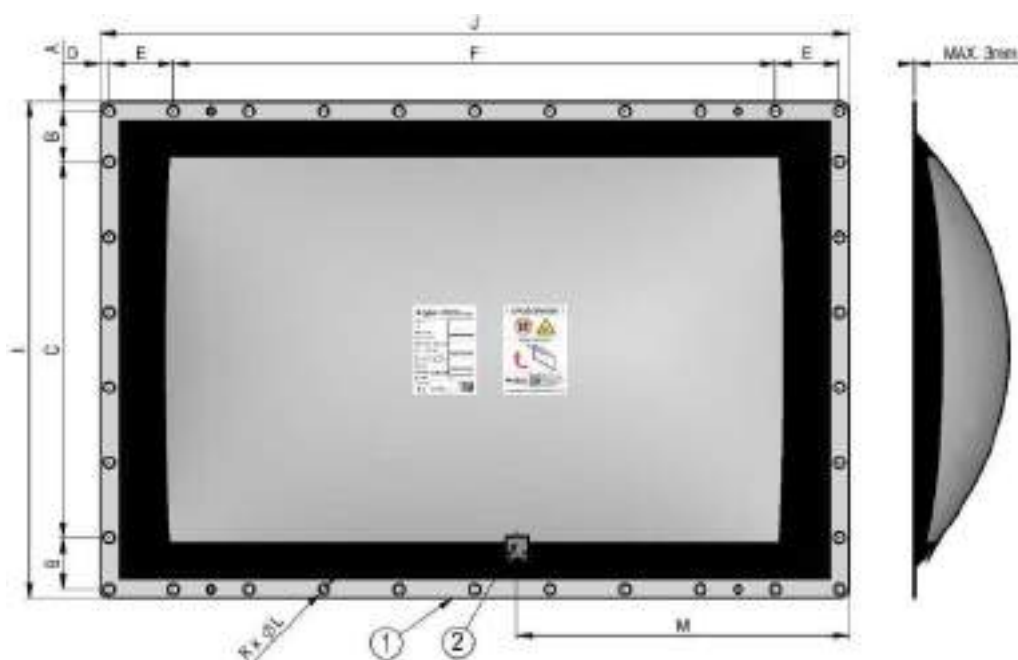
Габаритная схема для VMP тип D прямоугольного
